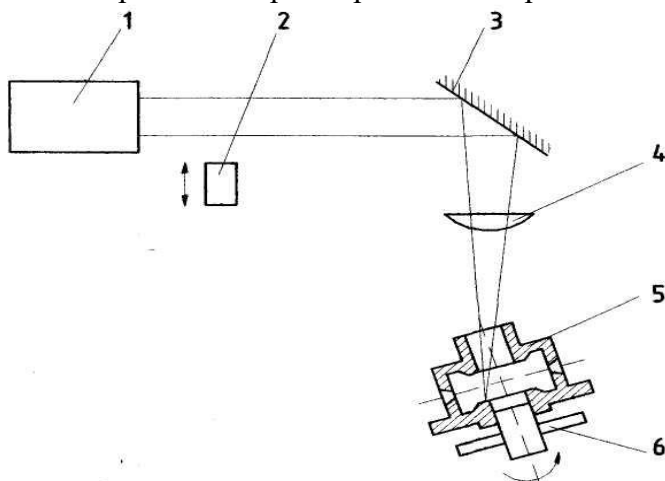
Схема обробки циліндричних поверхонь: 1 - лазер; 2 - вимірник потужності; 3 - дзеркала; 4 - фокусуюча лінза; 5 - деталь; 6 - пристосування.
